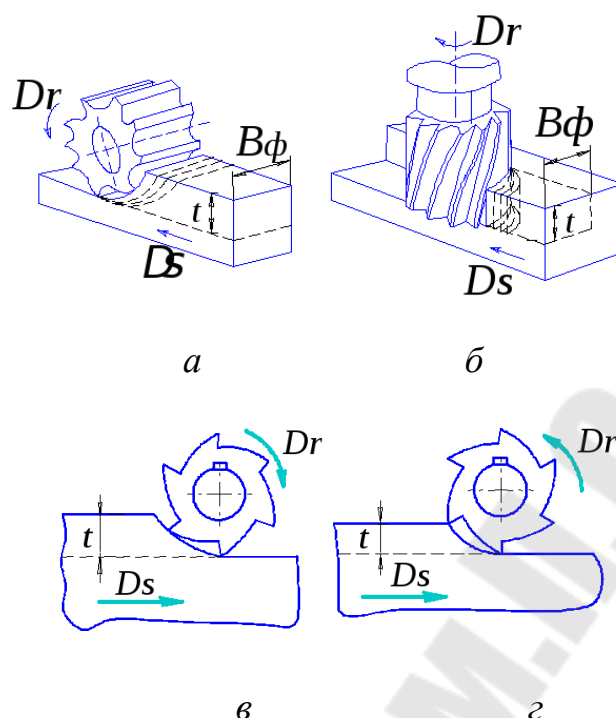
Фрезерование: *а* – периферийное (цилиндрическое) фрезерование; *б* – торцовое периферийное фрезерование; *в* – встречное периферийное фрезерование; *г* – попутное периферийное фрезерование
